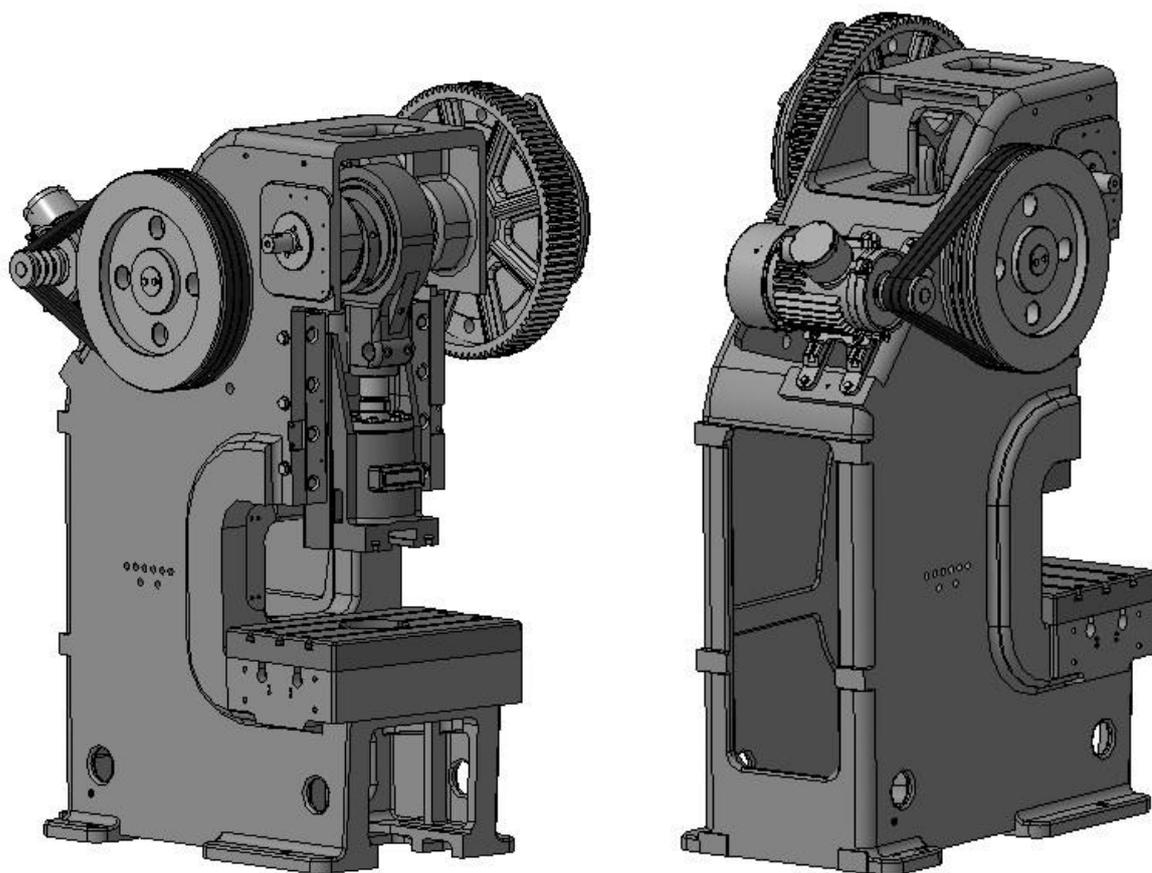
Сборочная 3D-модель прессы однокривошипного K2130B
